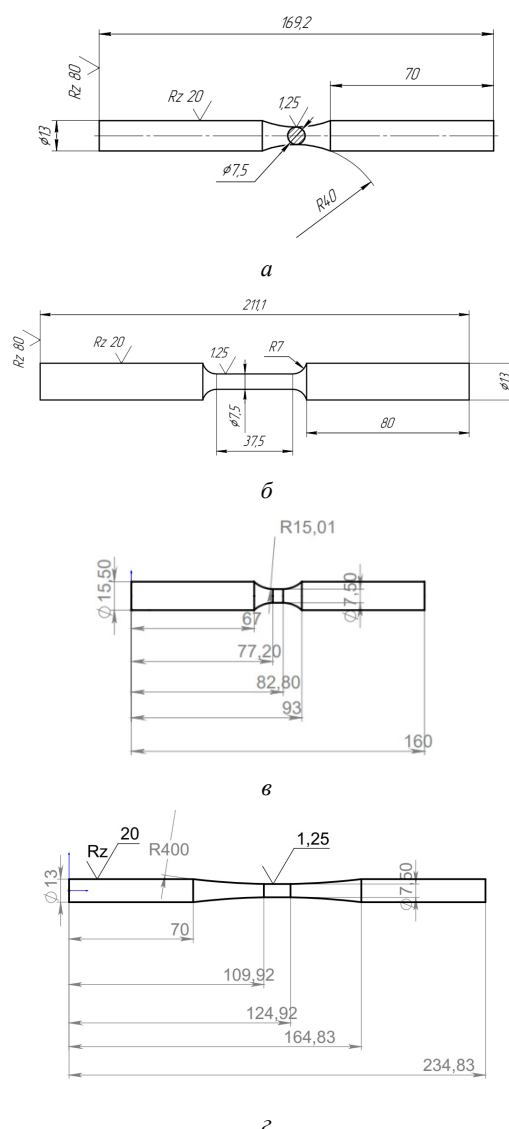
Образцы с различной геометрией: а – образец № 1 (тип I по ГОСТ 25.502-79); б – образец № 2 (тип II по ГОСТ 25.502-79); в – образец № 3; г – образец № 4
